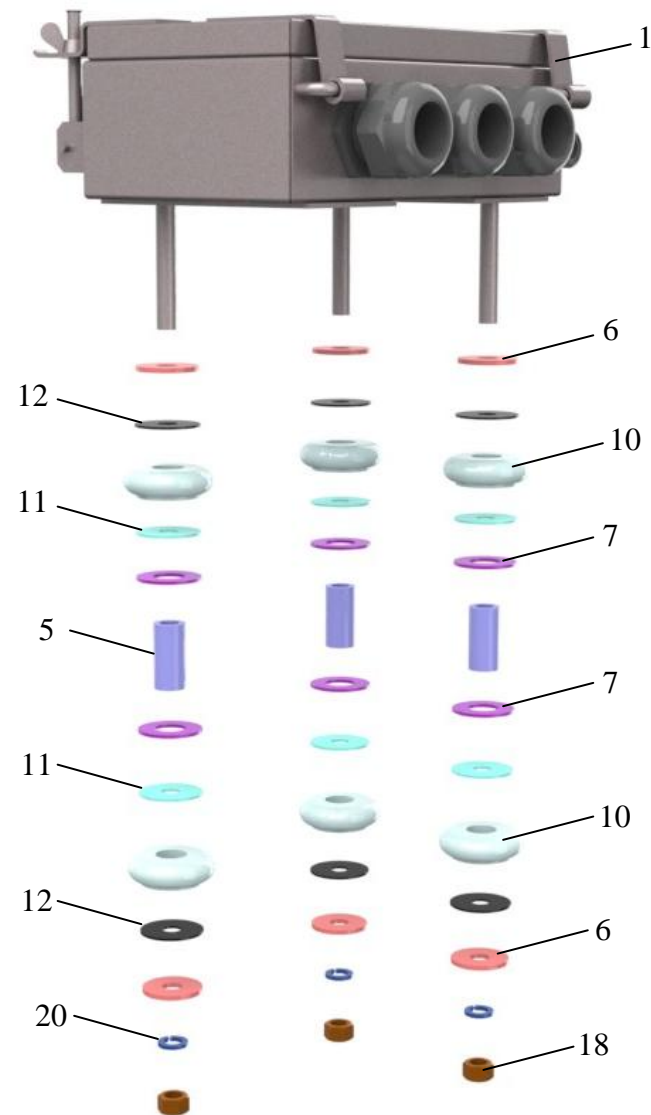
Установка коробки вводной АКСМ 321-340500.000
